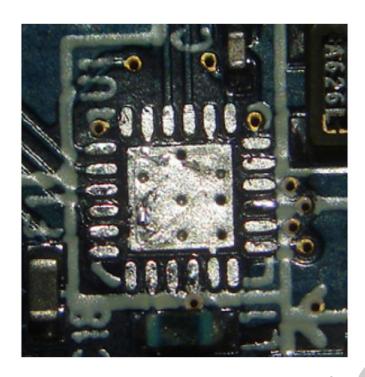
Islas sucias de soldadura y flux
